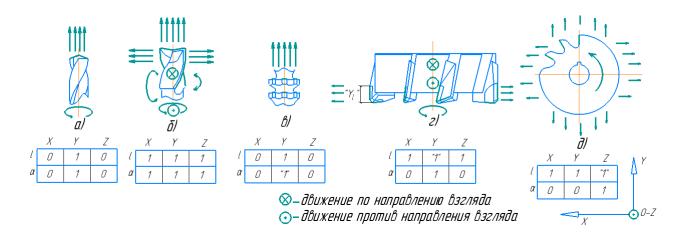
Движения осевого инструмента и их отображение в виде шестиклеточных таблиц: а) сверла; б) концевой фрезы; в) круглой протяжки; г) торцевой фрезы; д) дисковой/цилиндрической фрезы
